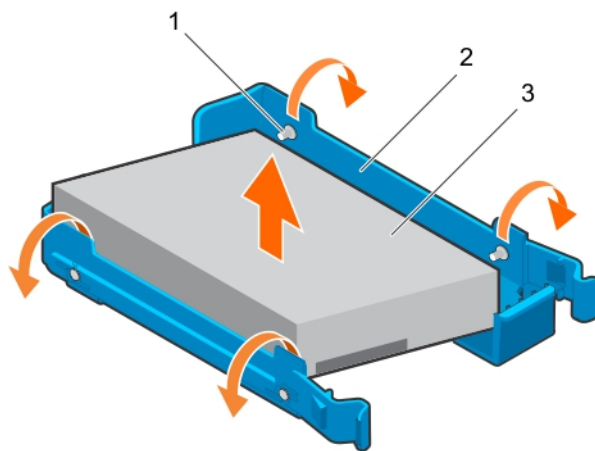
Entfernen und Installieren eines Festplattenlaufwerks aus/in einem Laufwerksträger
